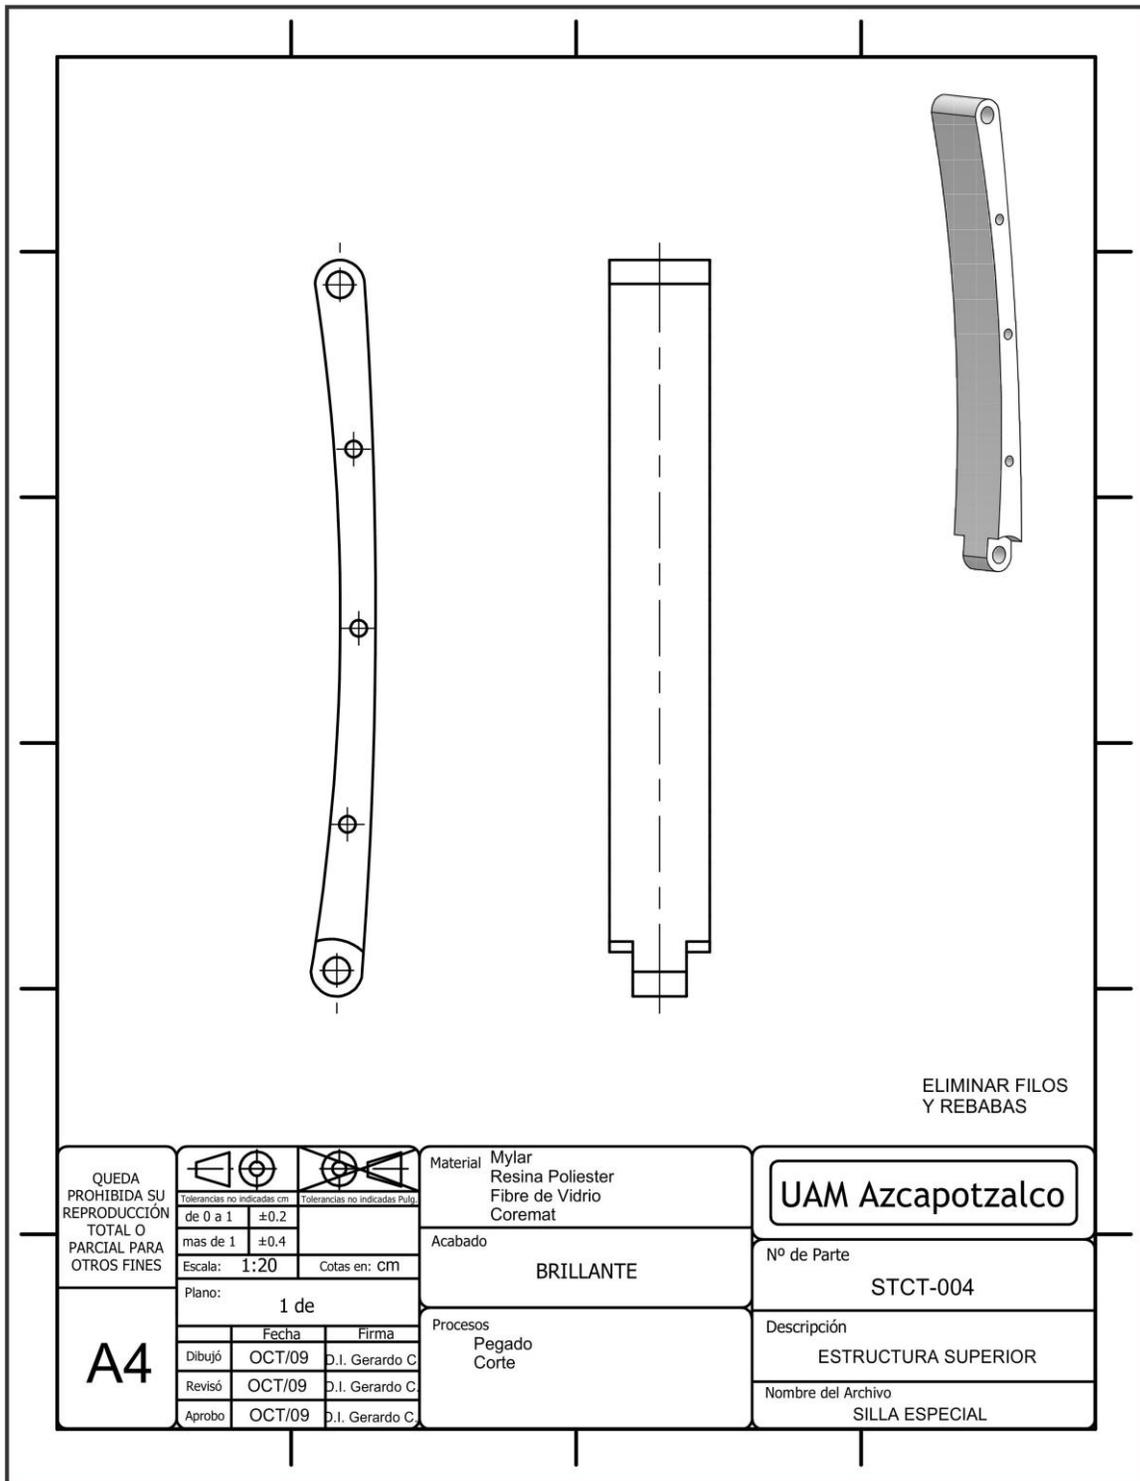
Planos de producción: estructura superior. Propuesta del Autor.
